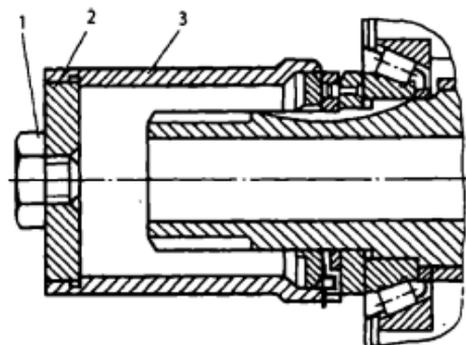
Спеціальний ключ И-801.41.000 для зняття гайки вальниць ведучого вала конічної шестірни середнього моста
